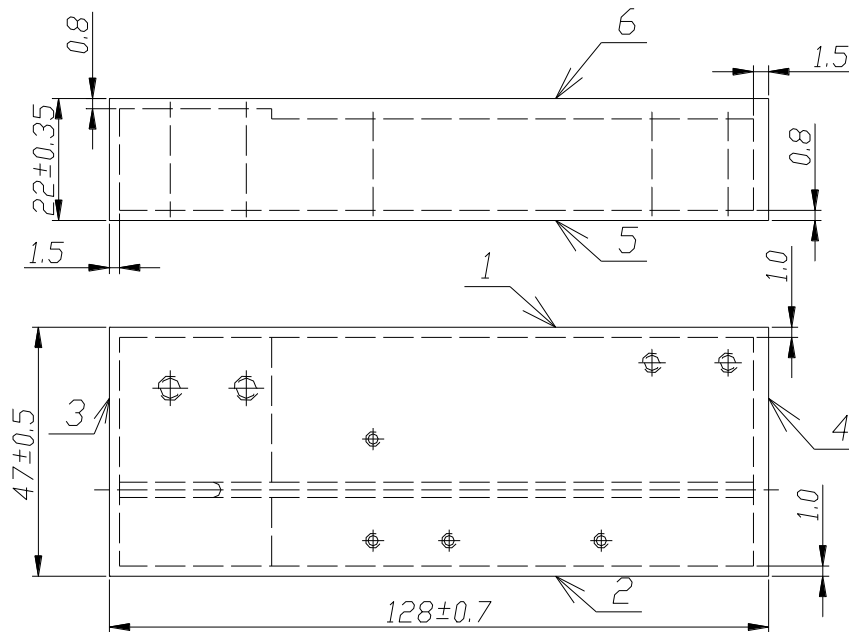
Заготовка деталі з нарахованими припусками і допусками
